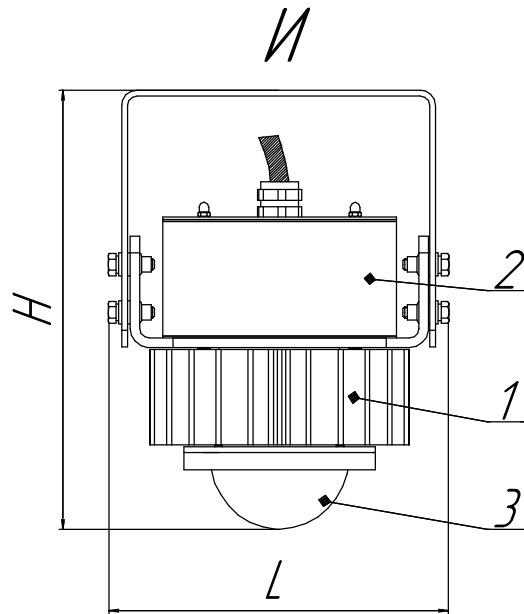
Внешний вид и габаритные размеры ДСП04-35-001.
